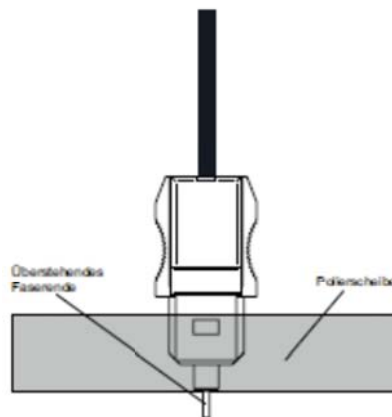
Steckermontage Schritt 2/ Cable assembly step 2
